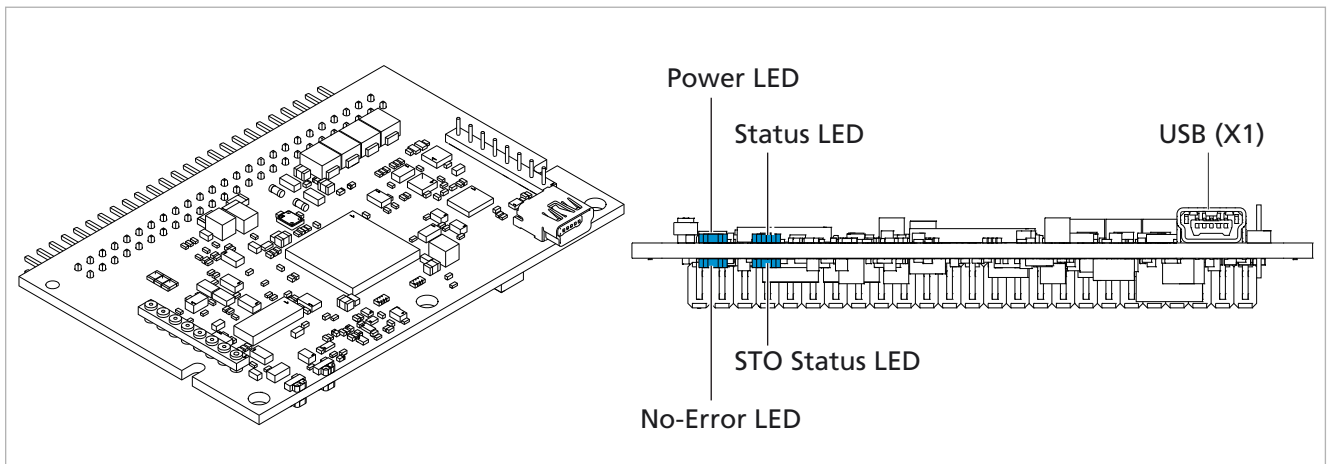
Isoansicht (links) und Frontansicht (rechts) der Standardplatine
